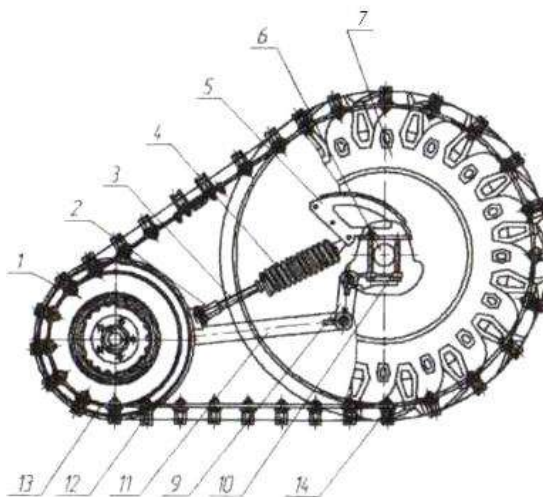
Полугусеничный движитель с резинометаллической гусеницей и штампованными почвозацепами
